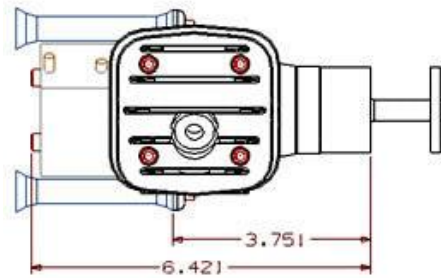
Vista en planta DA 50(Fuente: Desert aircraft)
